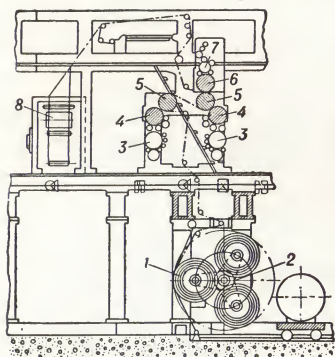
Схема секции ротационного газетного агрегата ГА: 1 — рулон бумаги; 2 — ролевая звезда; 3 — основные красочные аппараты; 4 — формные цилиндры; 5 — печатные цилиндры; 6 — формный цилиндр второй краски; 7 — красочный аппарат второй краски; 8 — фальцевальный аппарат. Пунктиром показан путь бумажного полотна.
